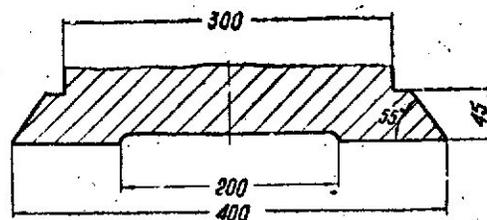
а. Эскиз направляющих станка модели 6М83Ш
